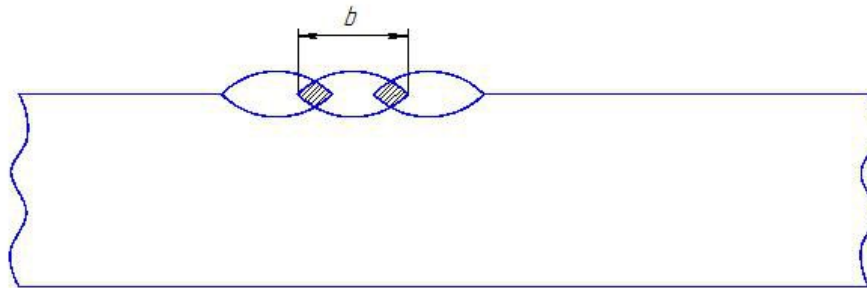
Наплавка с различным шагом в долях от ширины наплавленного металла.
